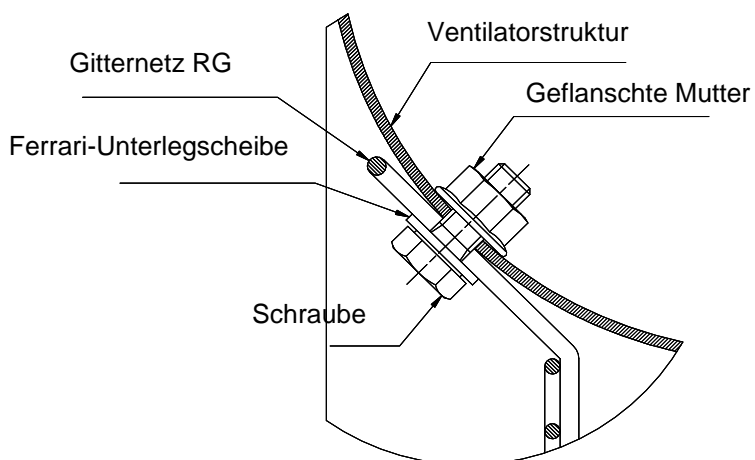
Montageplan der Schutzeinrichtung RG
